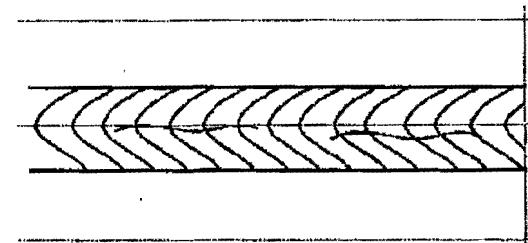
24. Продольная трещина сварного соединения
